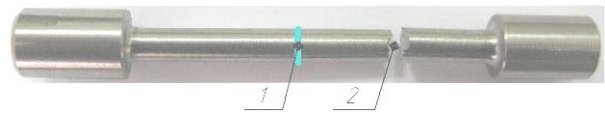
Образец после испытаний на растяжение: 1 – сварной шов; 2 – место разрушения
